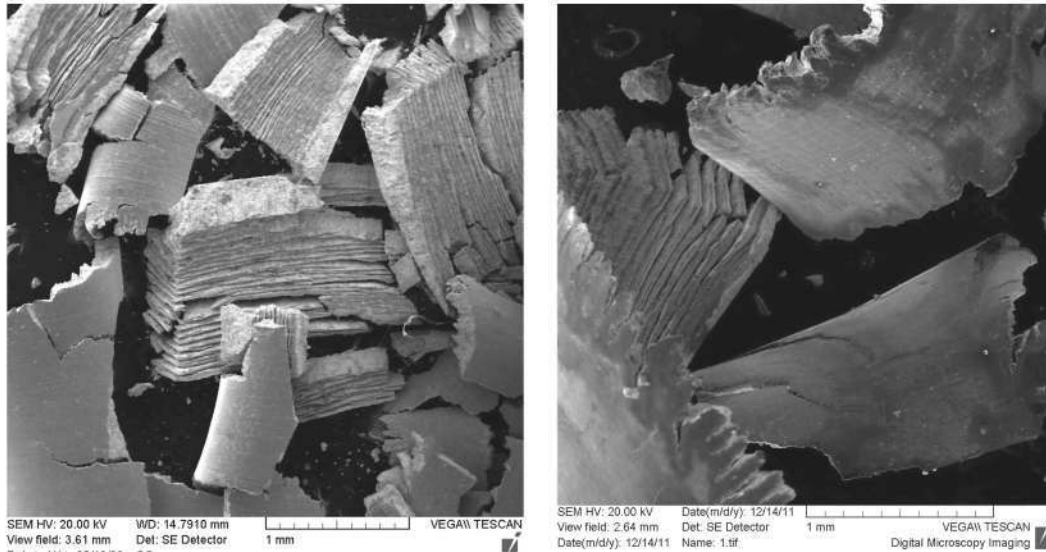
Стружка твердого сплава перед атриторной обработкой
